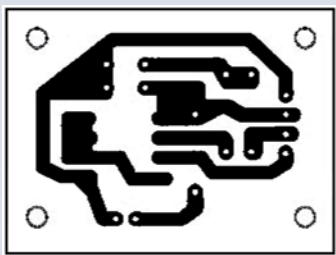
PCB Scheda accelerometro lato componenti (scala 1:1).
